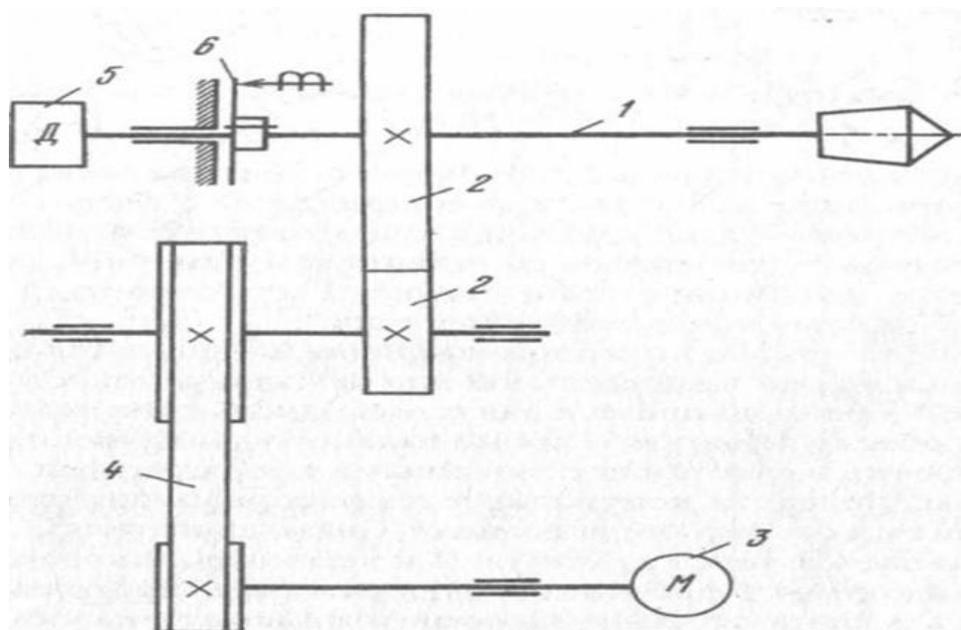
Однодвигательный привод с режимом контурной обработки.
